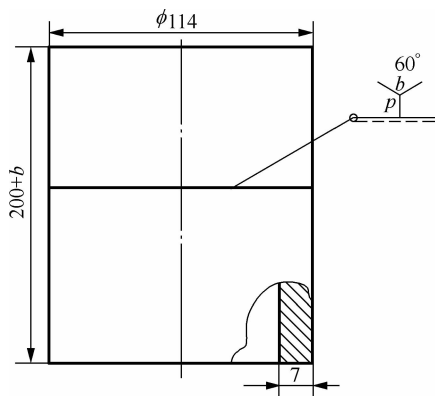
钢管对接环焊缝 CO_2 气体保护焊装配图
